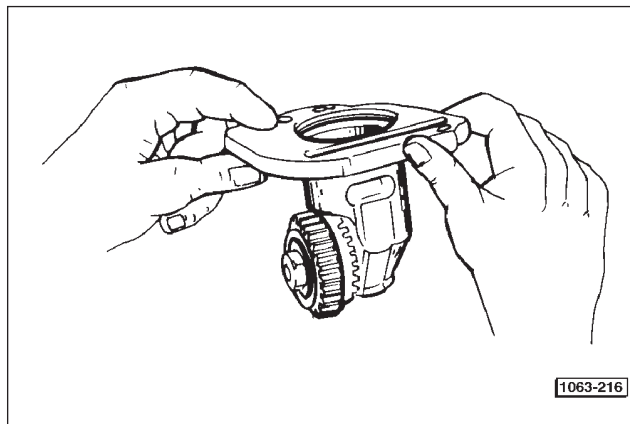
SEULEMENT POUR TRACTEURS EQUIPES DE RÉGULATEUR MECANIQUE - Assembler le renvoi à équerre de commande de régulateur moteur et de pompe à huile. Pour l'assemblage et l'ajustage faire référence aux instructions à la page 60.
